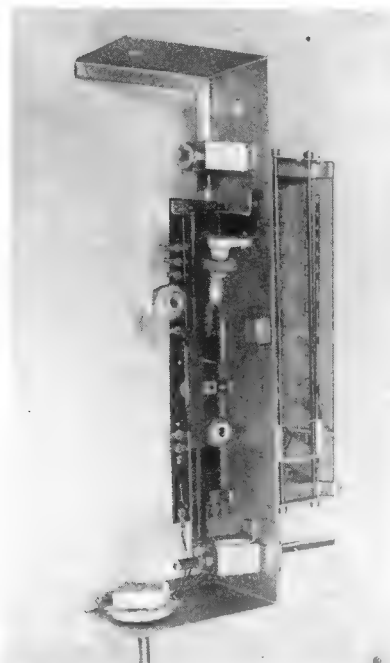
Rückansicht des U-förmigen Aggregatträgers
